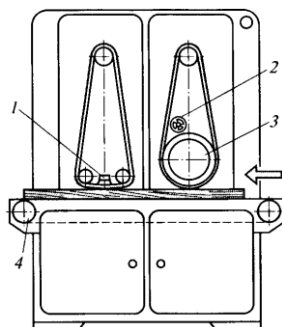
Широкострічковий шліфувальний верстат з верхнім розташуванням агрегатів: 1, 3 – шліфувальні агрегати; 2 – маховичок настроювання на товщину зішліфовуваного шару; 4 – конвеєр
